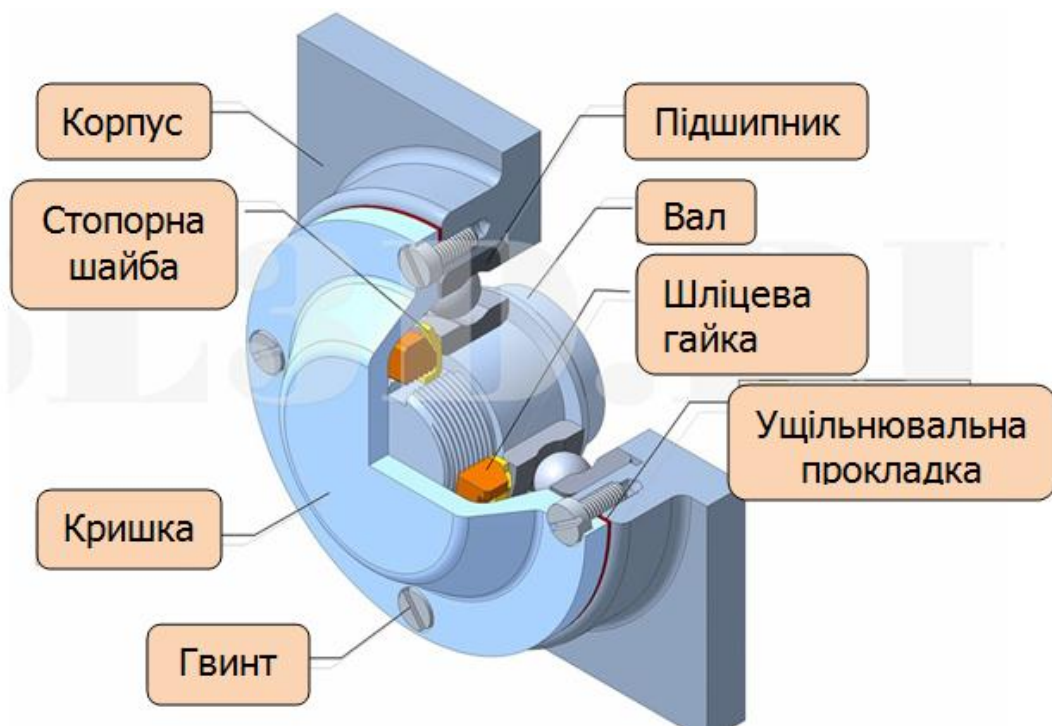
Установка підшипника з зазором з фіксацією при допомозі кришки
